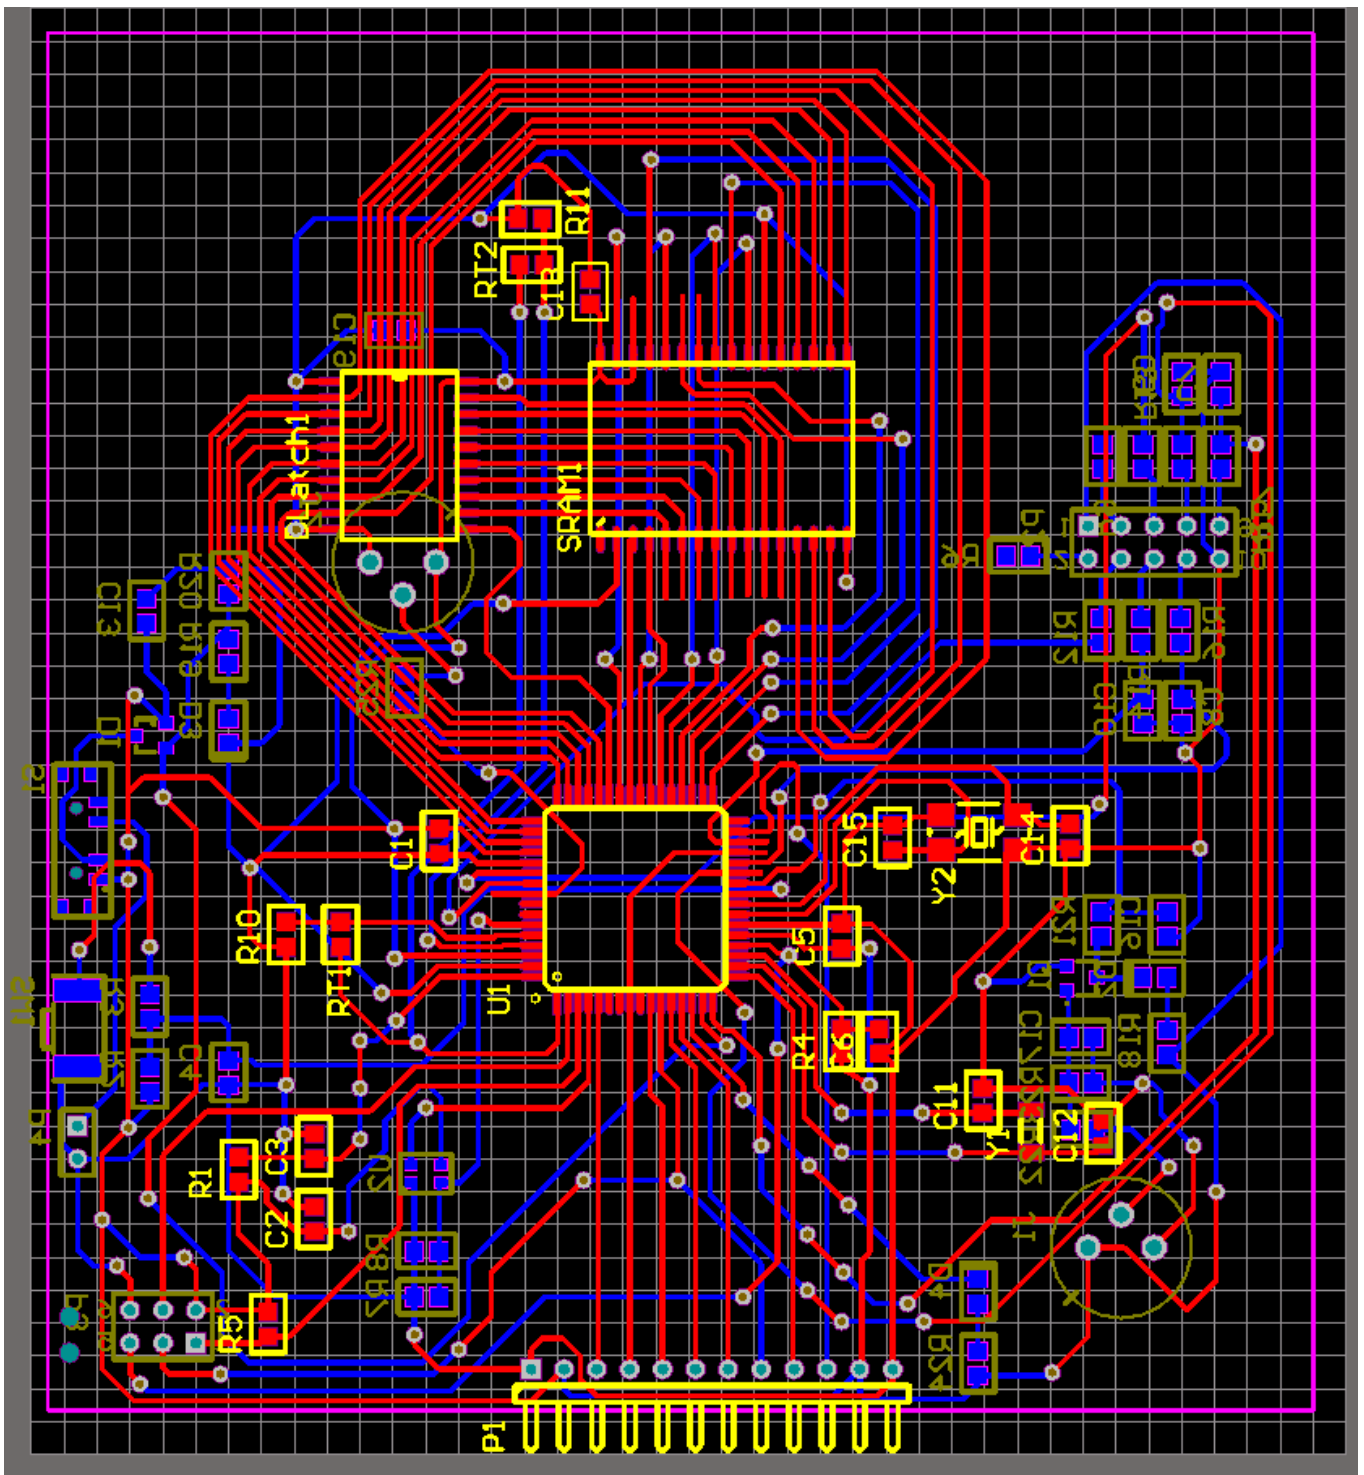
Diseño PCB del dispositivo DAS220.5
